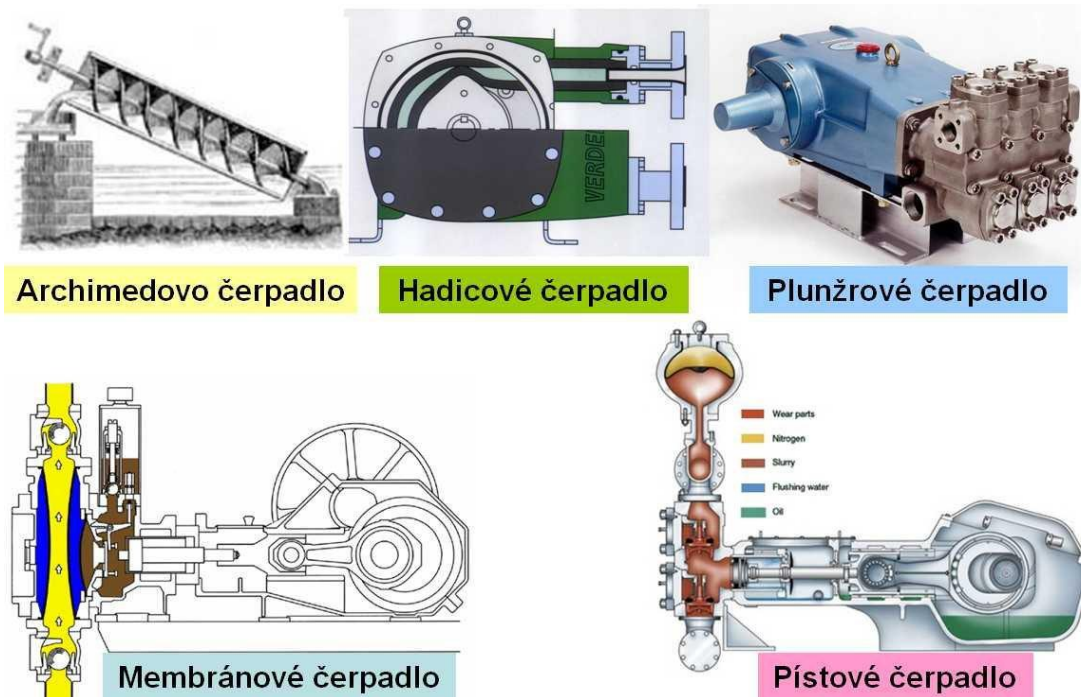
Některá vybraná objemová čerpadla [1]
